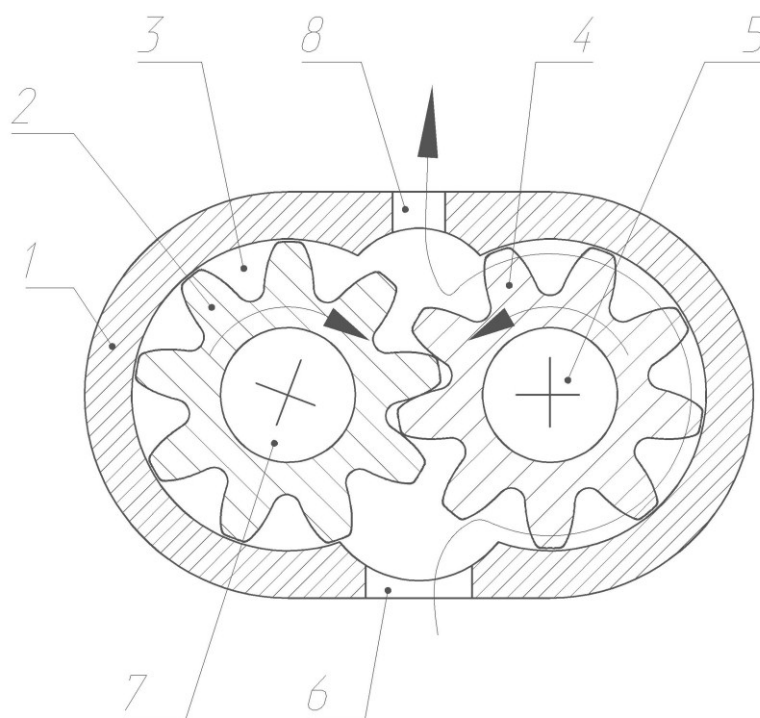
Схема шестеренного насоса: 1- корпус; 2- шестерня; 3 – полость между зубьями (элементарный рабочий объем); 4 – шестерня; 5 – ось; 6 – всасывающая полость; 7 – вал; 8 – нагнетательная полость.
